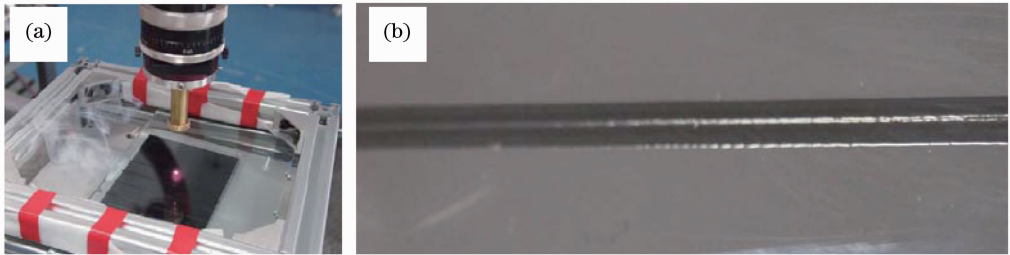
(a) PMMA激光穿透焊接; (b) 焊缝
